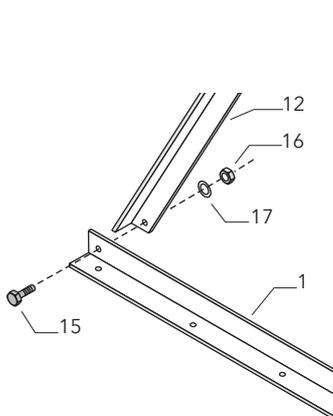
Kollektorprofil mit Bodenprofil verschrauben.
